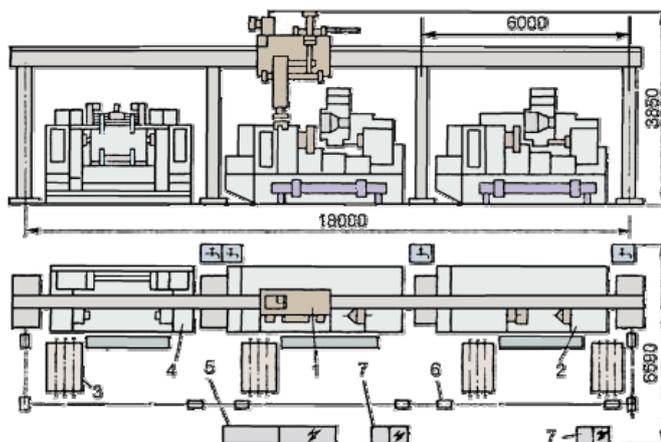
РТК для механической обработки заготовок типа «вал»
